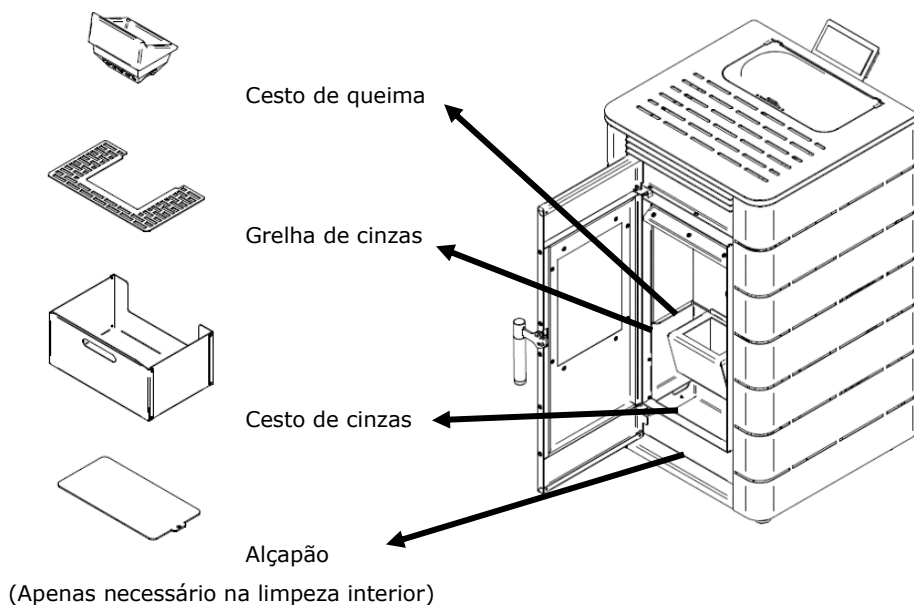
Acessórios a retirar na limpeza do equipamento E100
